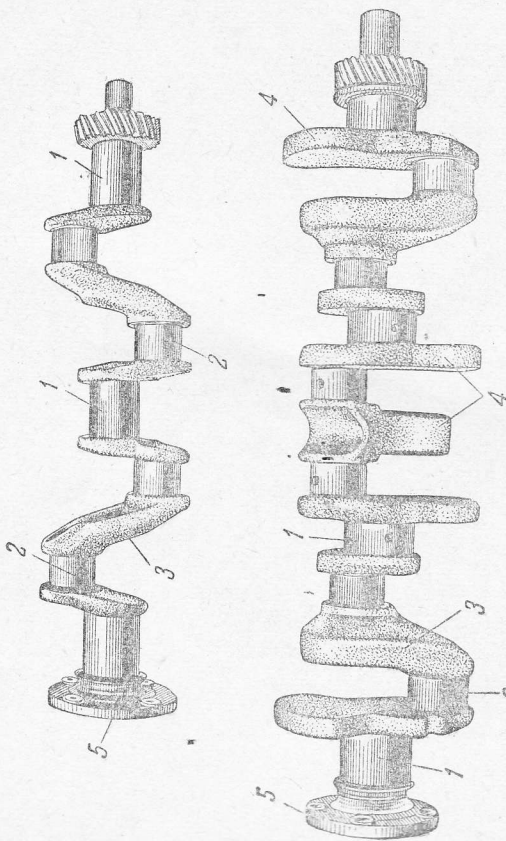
Коленчатые валы четырех и шестицилиндровых двигателей:
